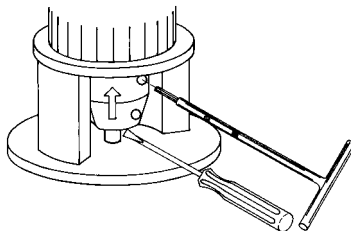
Dvíhanie spojky a hriadeľa čerpadla
